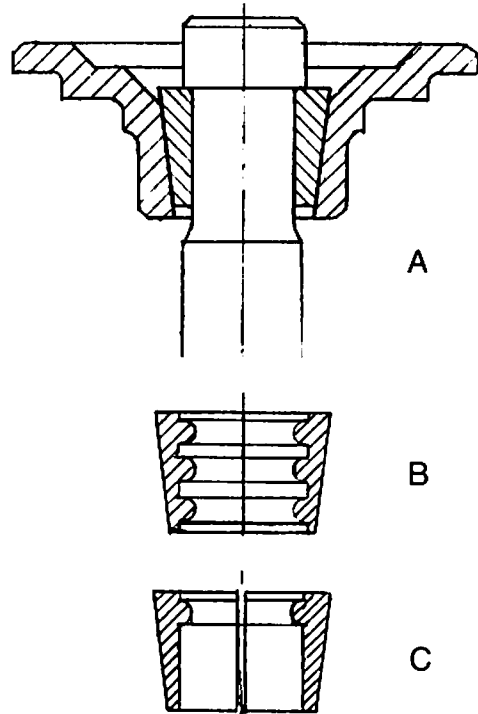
Geteilter Ventil-Klemmkegel für Federteller.
